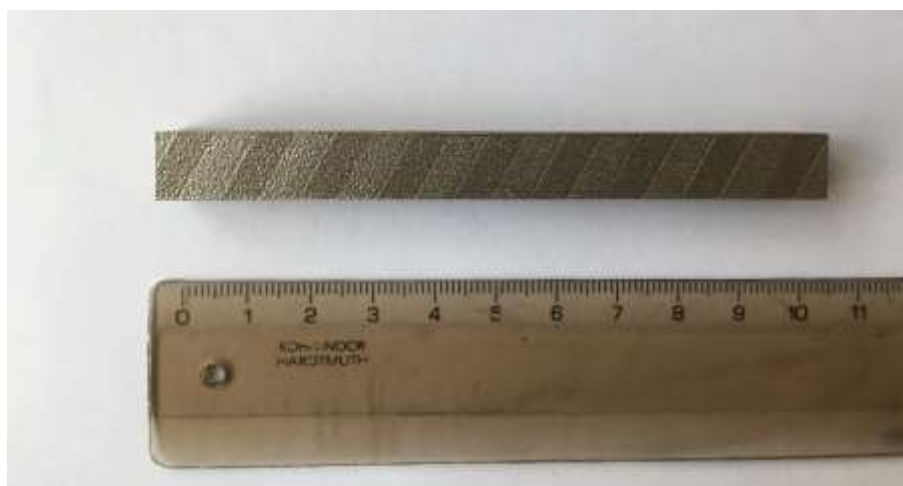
Горизонтальный образец из сплава Co-Cr-Mo, изготовленный на 3D-принтере (вид сверху)
